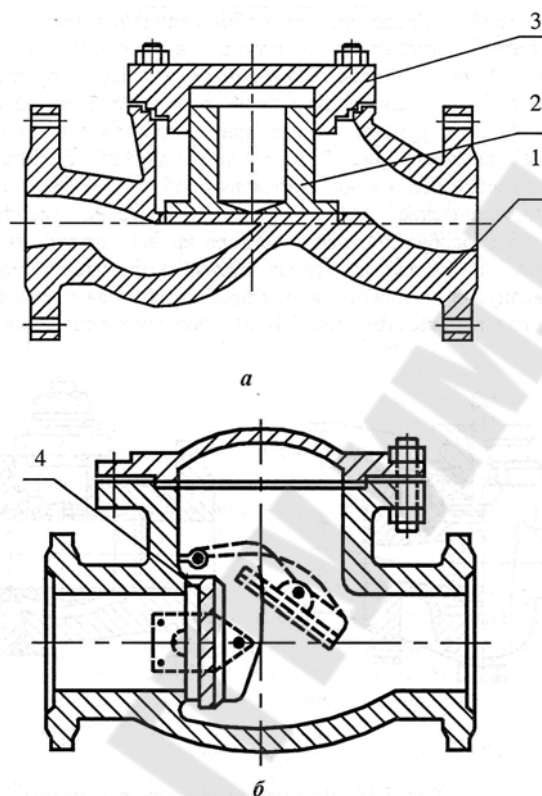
Обратные фланцевые клапаны: а - подъемный, тип 1бч3бр; б - поворотный, тип 19ч1ббр; 1 - корпус, 2 - подъемный затвор, 3 - крышка, 4 - поворотный затвор
